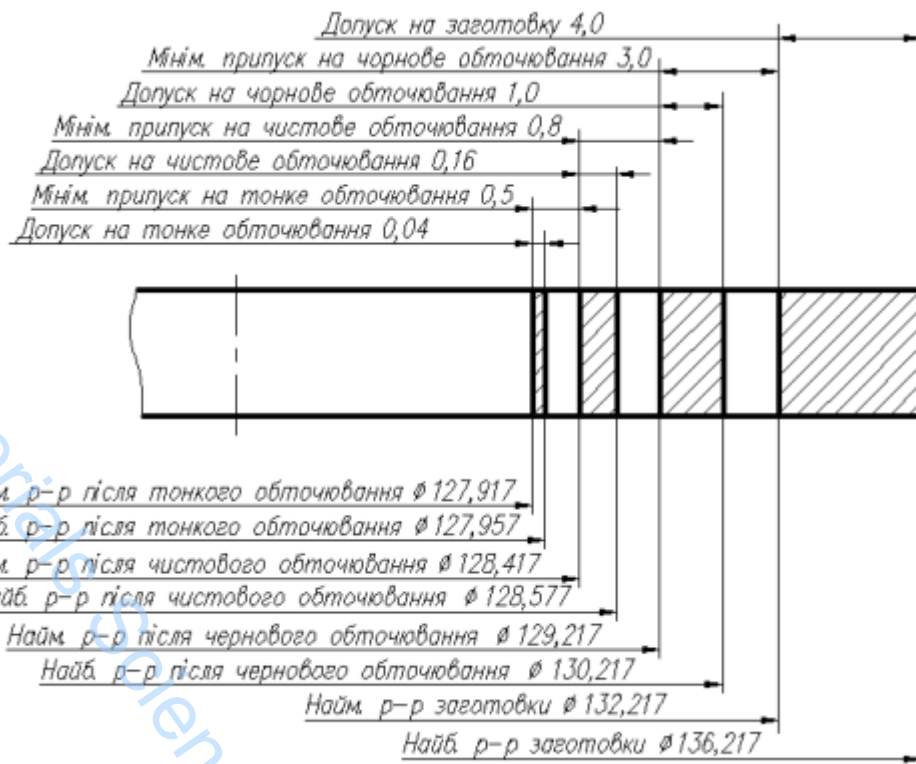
Схема розташування припусків і допусків при обробці поверхні головки $\varnothing 128f7 \begin{matrix} (-0,043 \\ -0,083) \end{matrix}$
